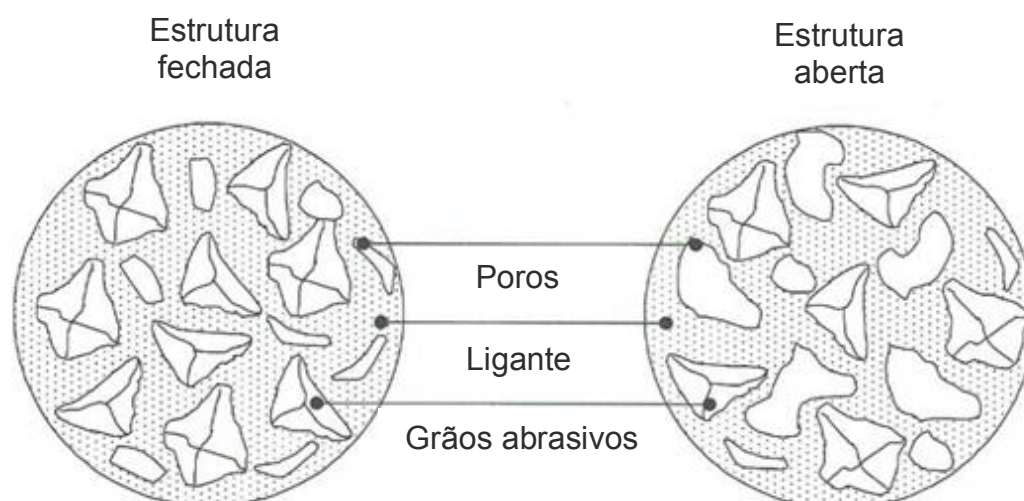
Estrutura de um rebolo de retificação (PORTO, 2004 - adaptado).
